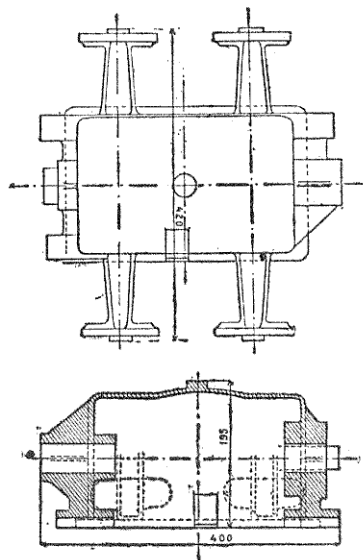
Carter pour moteur 2 cylindres obtenu par moulage mécanique.
